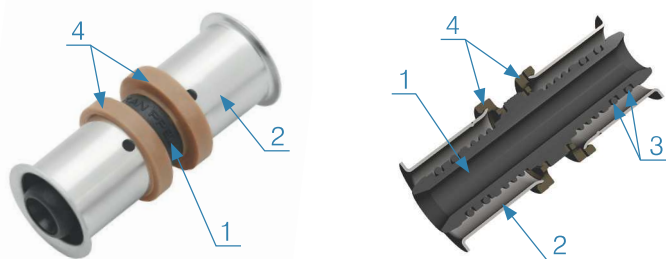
Общий вид и вид в разрезе соединителя KAN-therm Press LBP
